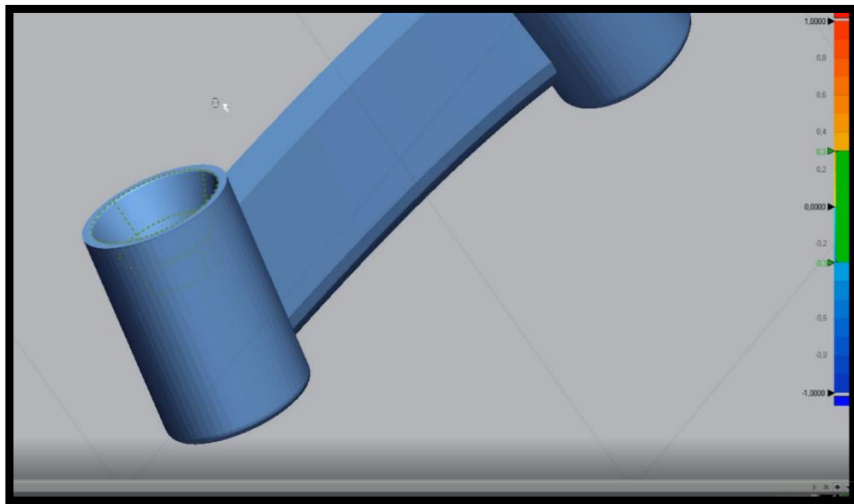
Cono proyectado en la superficie interna de la conexión de la barra. Plano sagital de la barra diseñada.
